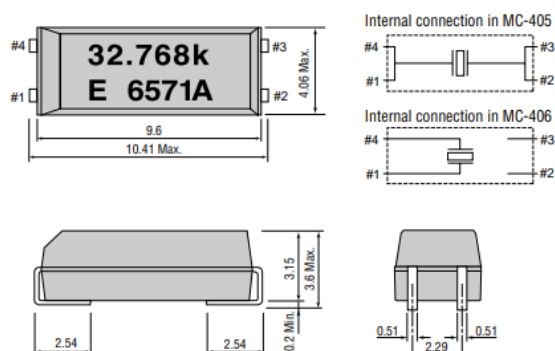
Габаритні розміри кварцового резонатора MC-405/MC-406
